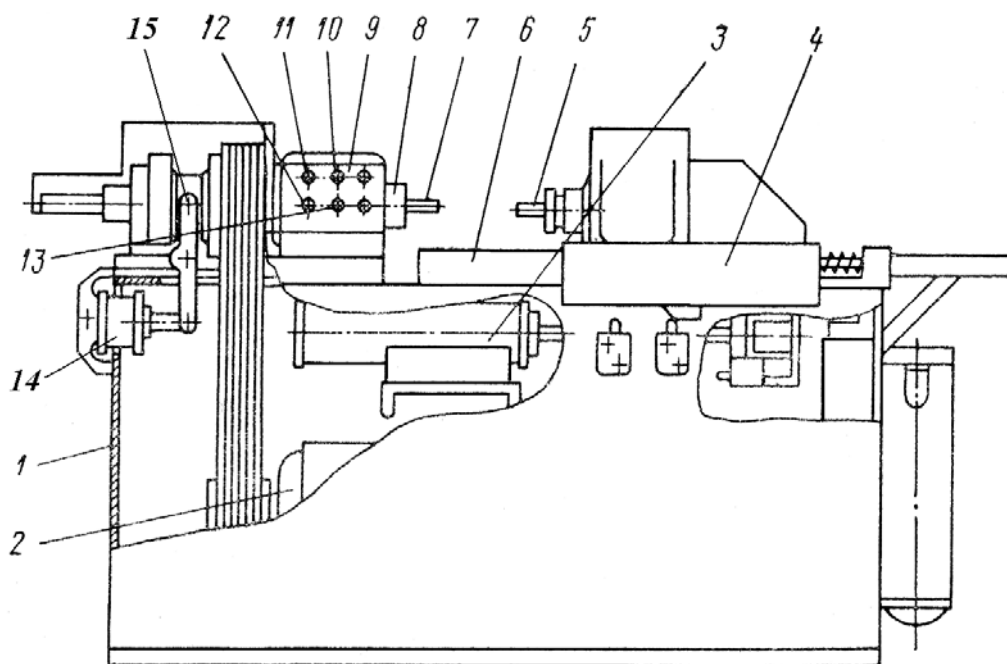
Общий вид специального сварочного полуавтомата мод. МФ-327:
